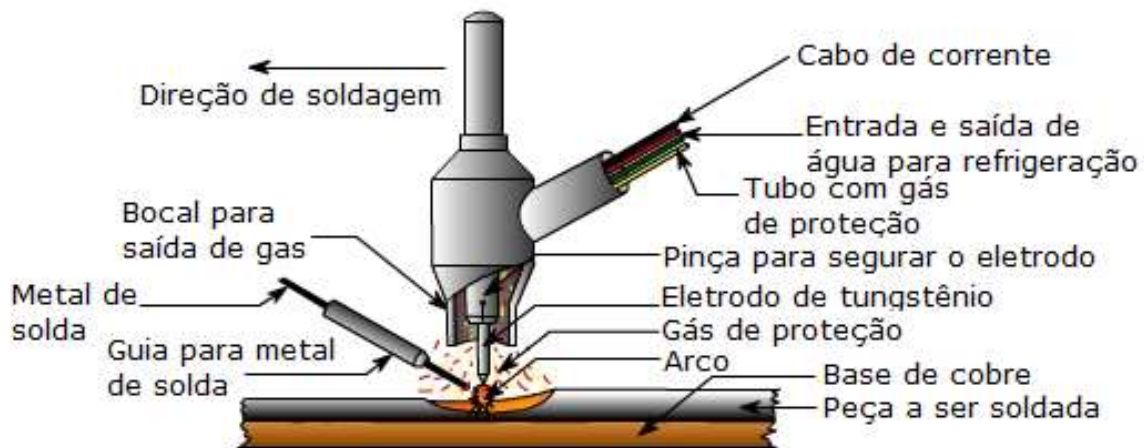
Esquema do processo de soldagem GTAW. Adaptado de [18].
